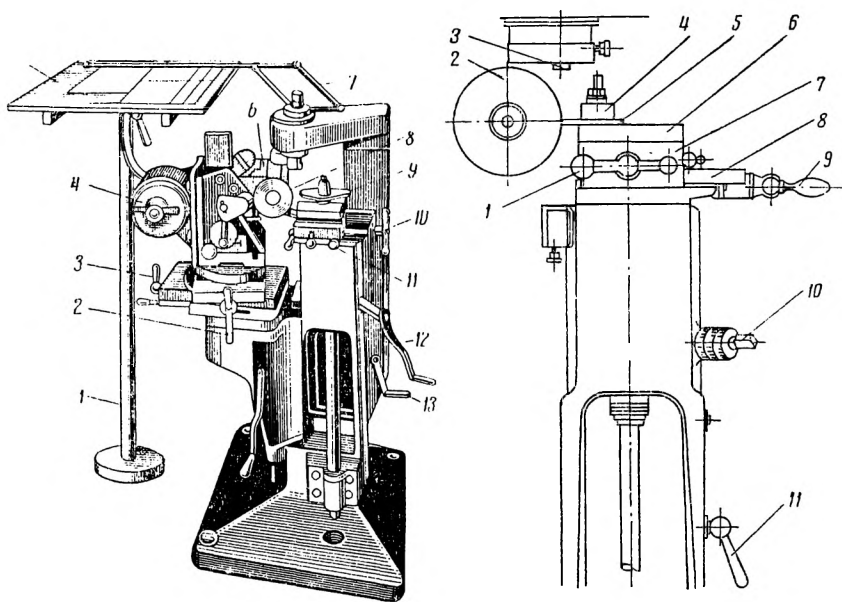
Оптический профилошлифовальный станок. Рис. 61. Суппорт для закрепления изделий
